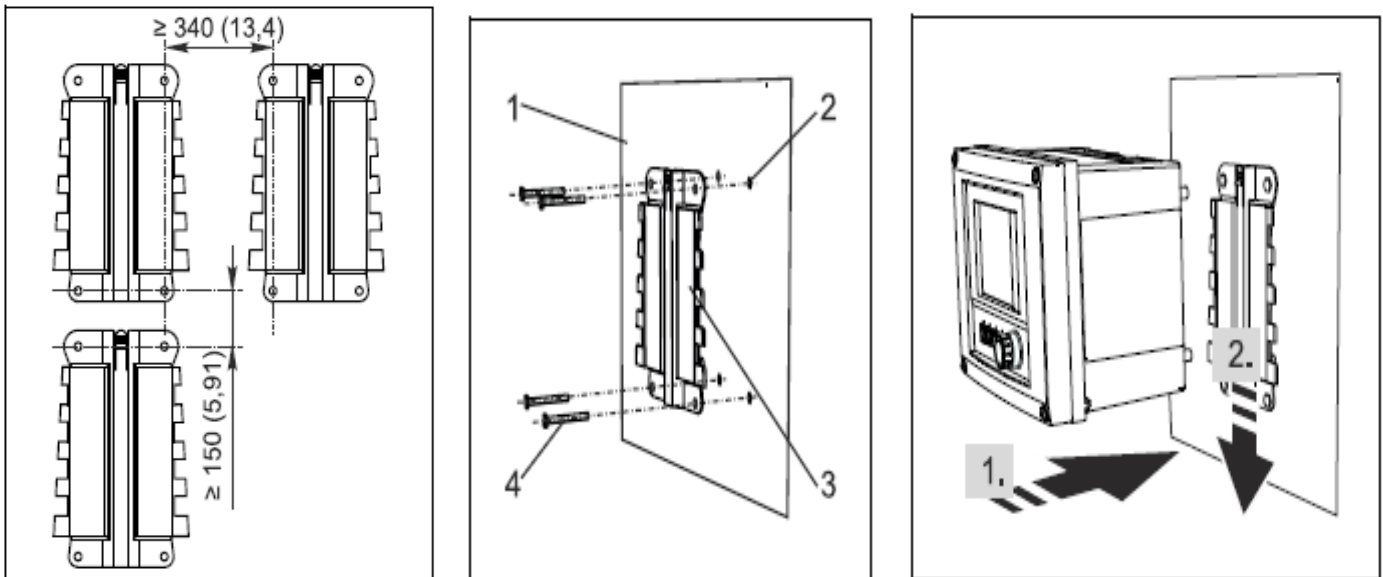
Dimensión del soporte y Montura a pared del transmisor M CM442.
